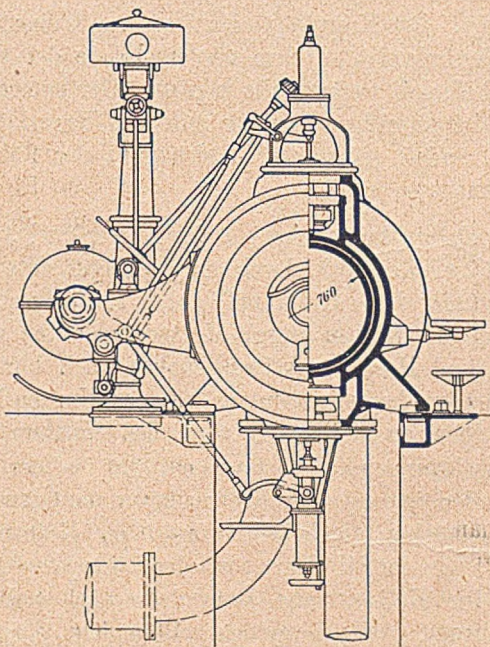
Verbunddampfmaschine der Zeche „Victor“. Steuerungseinrichtung des Hochdruckzylinders.
